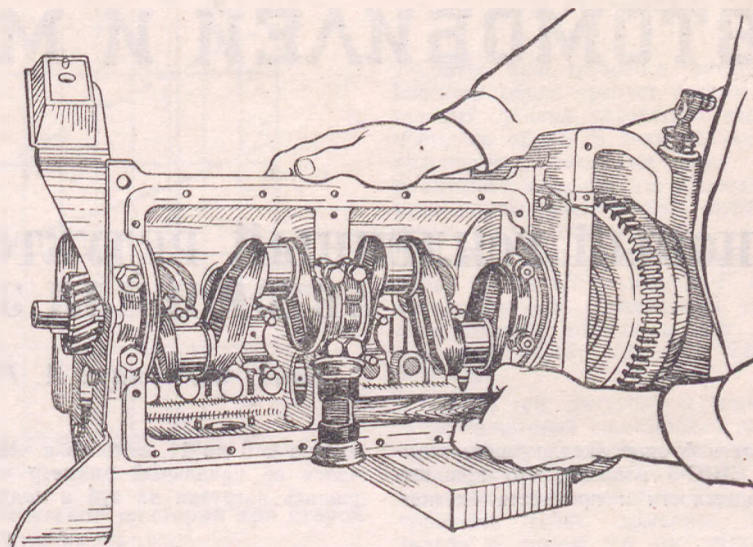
Поджатие крышки коренного подшипника к шейке коленчатого вала.
